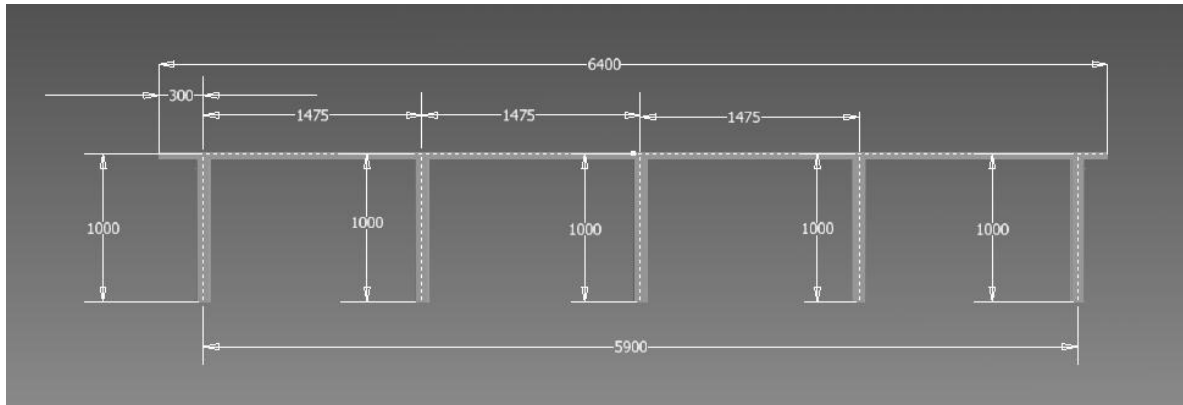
Disposición de los perfiles para el armado de la bancada.
